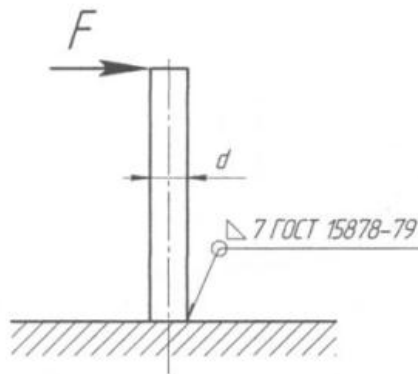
Розрахункова схема для визначення навантаження зварного шва основи
